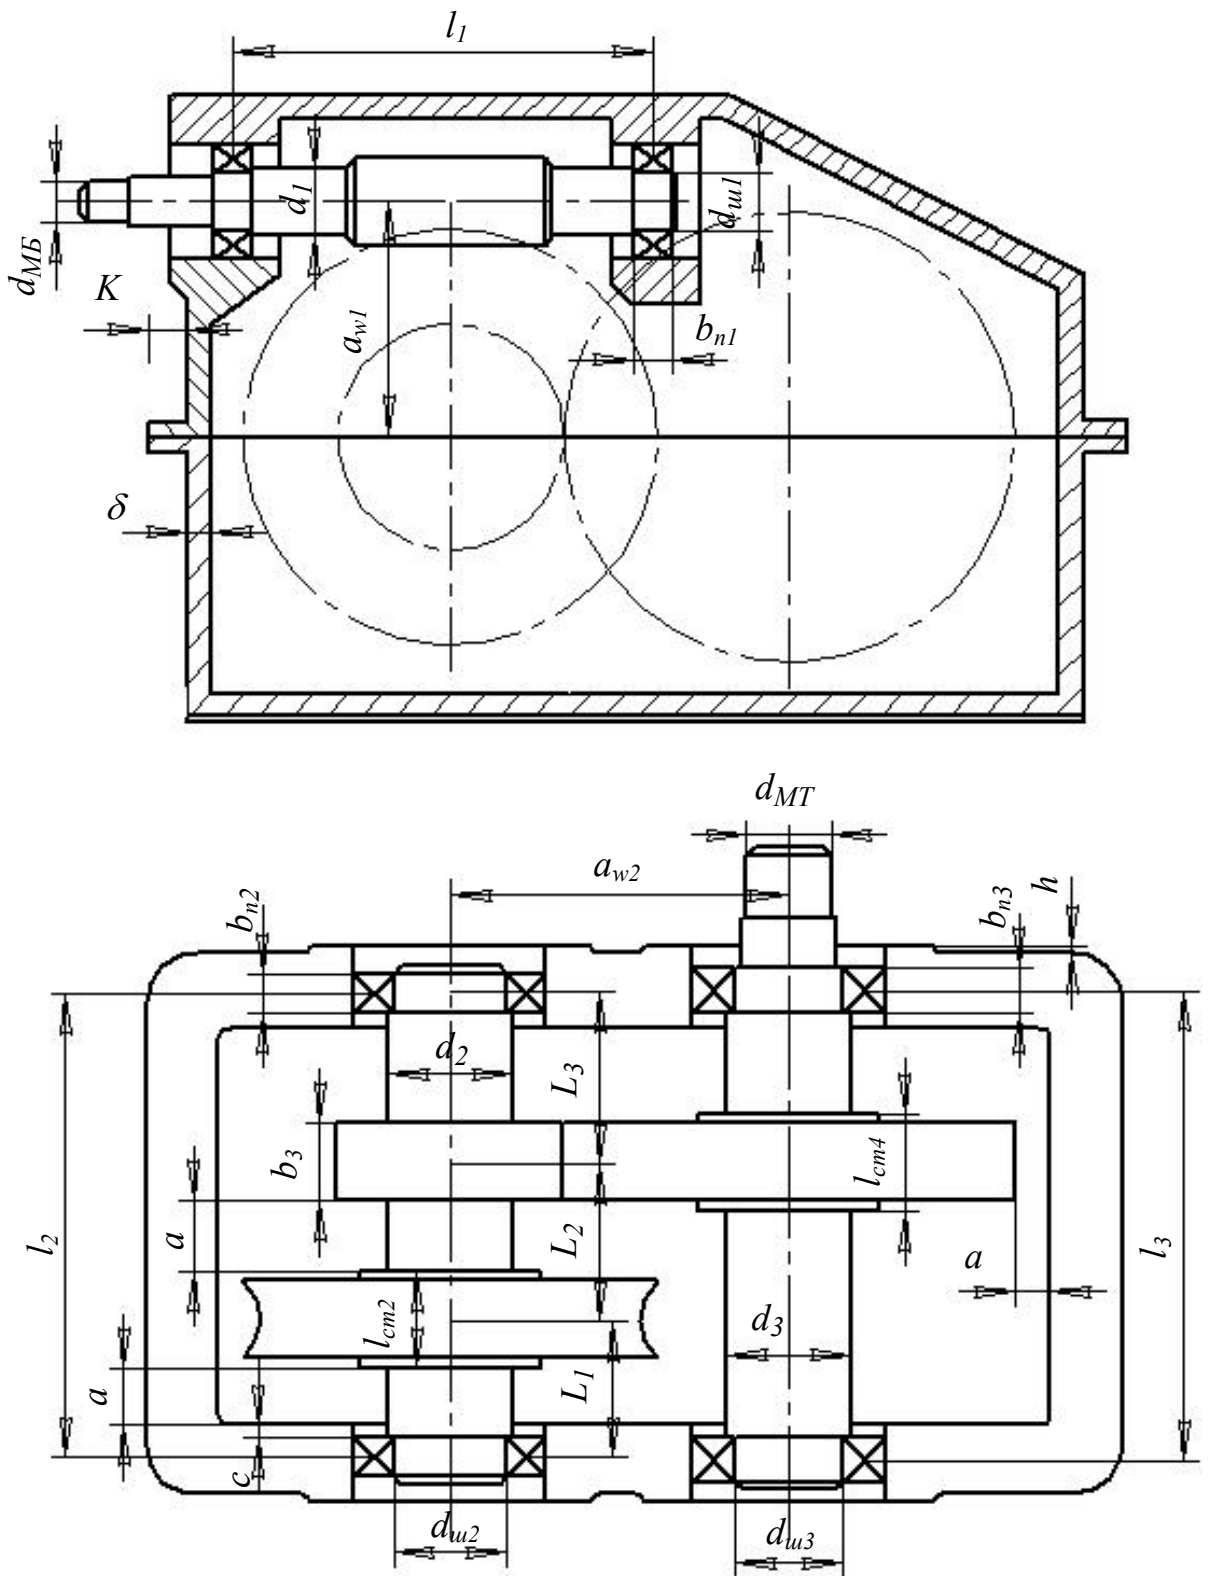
Ескізне компонування черв'ячно-циліндричного двоступеневого редуктора з верхнім розташуванням черв'яка
